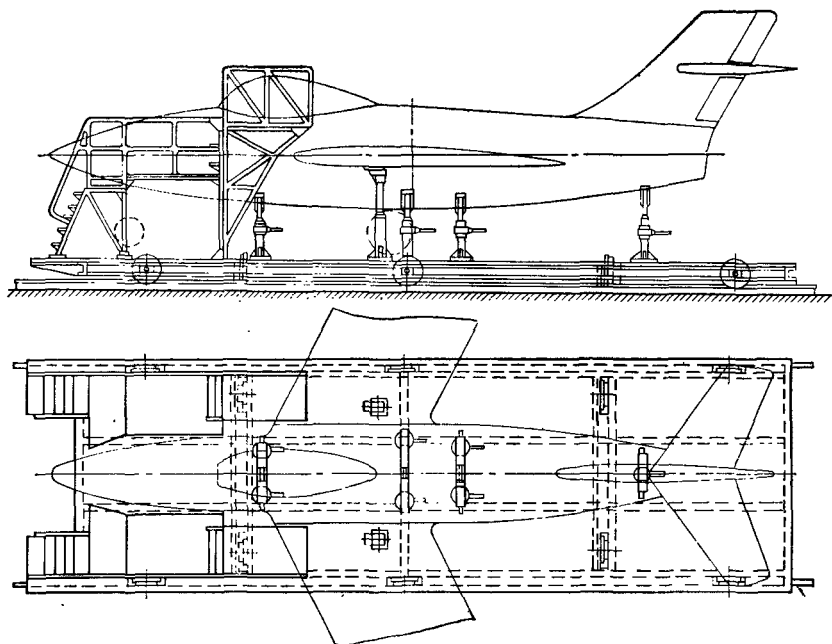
Конвейерная тележка для сборки легкого самолета с поперечными колесами для перемещения с одной линии на другую
